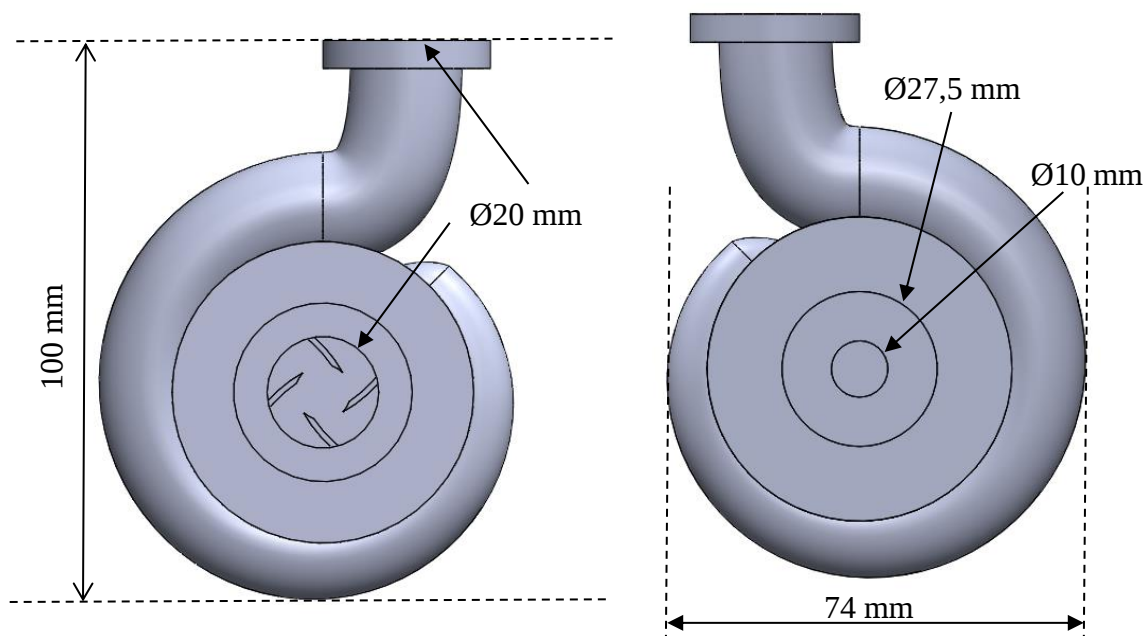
Bomba y motor, vista de la parte frontal y trasera
